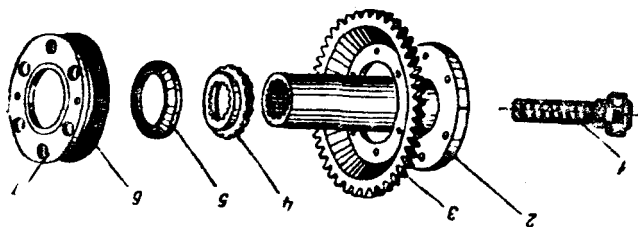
Привод магнето: 1—плунжер; 2—валик; 3—шестерня; 4—упорное кольцо с маслоотражателем; 5—уплотнительное кольцо; 6—прокладка; 7—опорное кольцо
